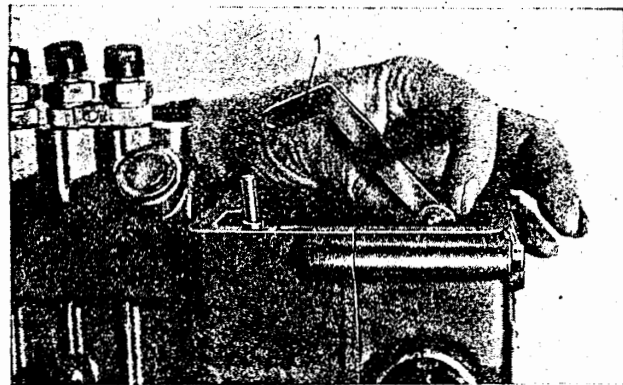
Aushängen der Stoßstange (1) an der Gelenkgabel
